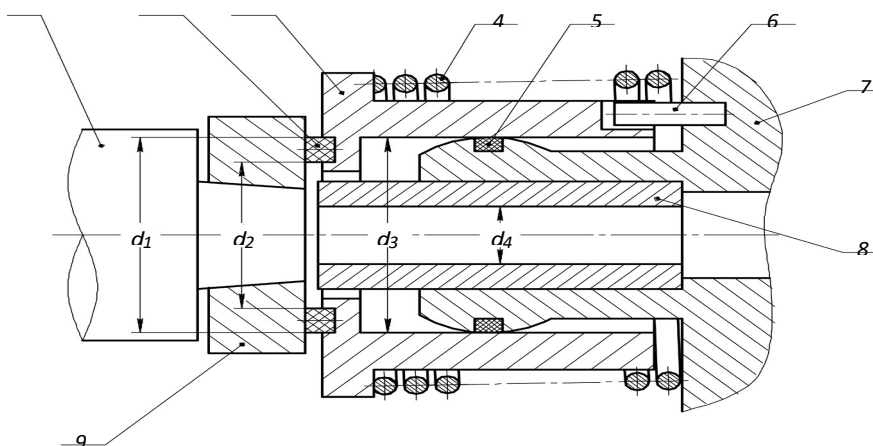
Торцевое уплотнение: 1 – заготовка; 2 – уплотнительный элемент; 3 – корпус уплотнения; 4 – пружина; 5 – кольцо уплотнительное; 6 – штифт; 7 – корпус маслоприемника; 8 – втулка кондукторная; 9 – втулка
